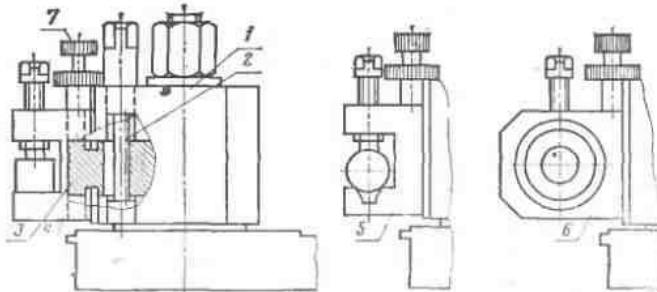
а. Резцедержатель двухпозиционный неповоротный
